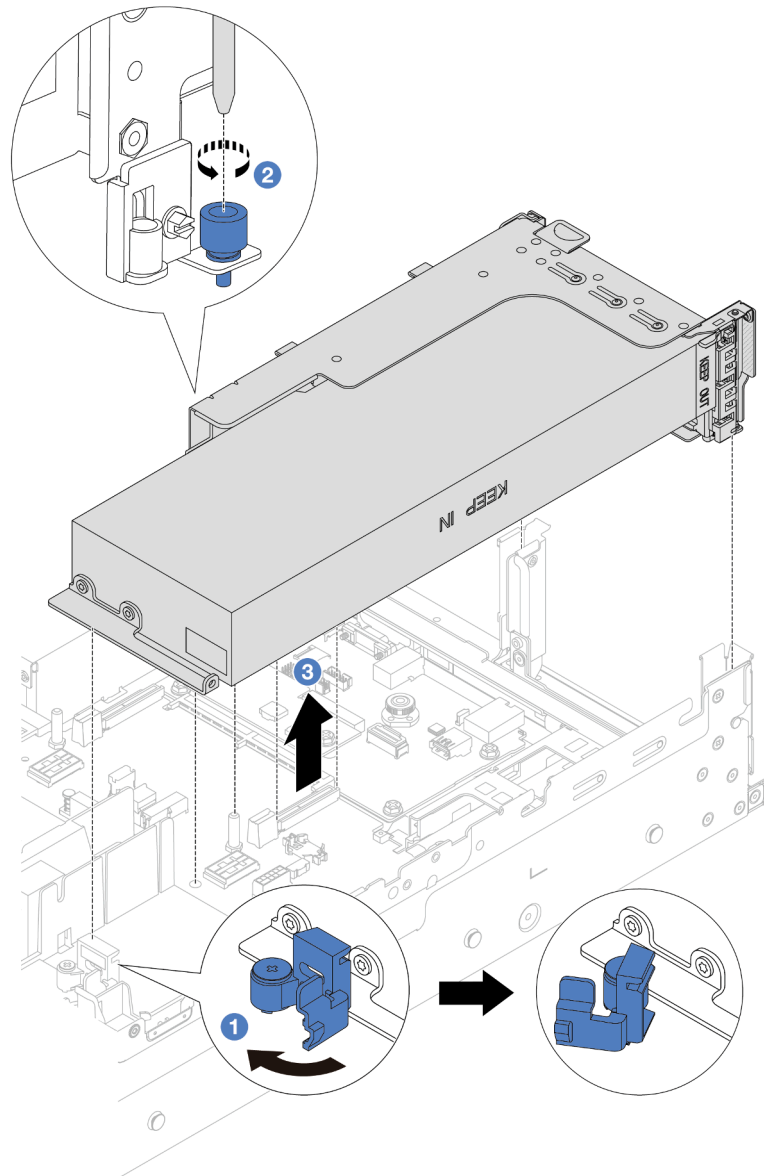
Entfernen der Adapterkartenbaugruppe 1 mit GPU-Adapter
